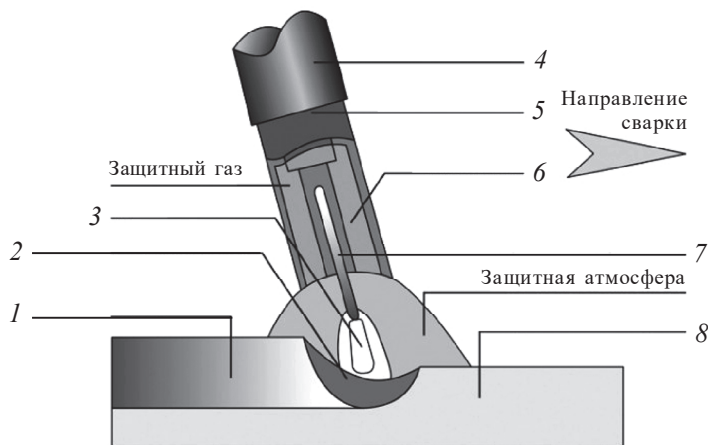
Полуавтоматическая сварка в среде защитного газа:
